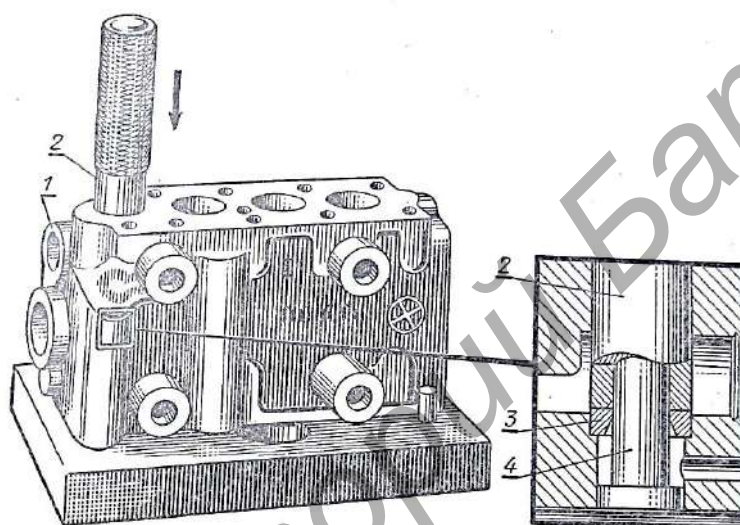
Запрессовка седла перепускного клапана: 1 – корпус распределителя; 2- оправка; 3 - седло перепускного клапана; 4 -направляющий стержень
